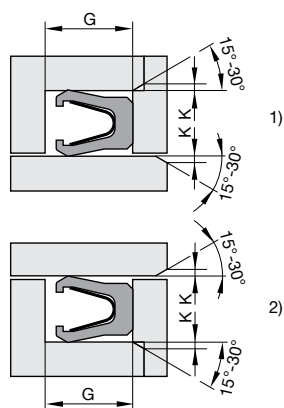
Установка составной посадочной канавки «губками вперед»;
